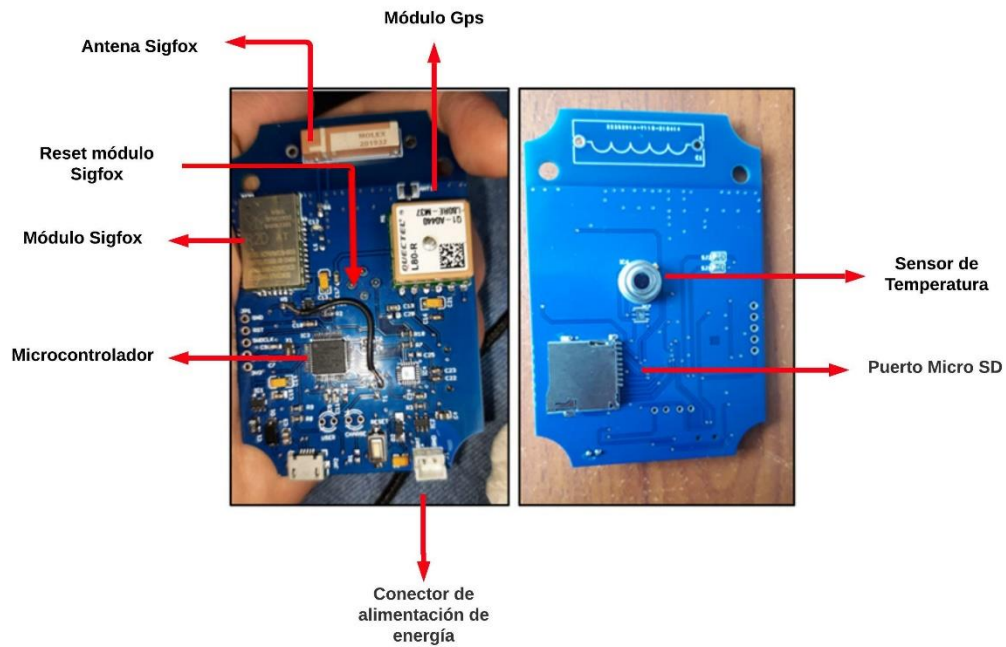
Segunda versión PCB ensamblado. Fuente Autor.
